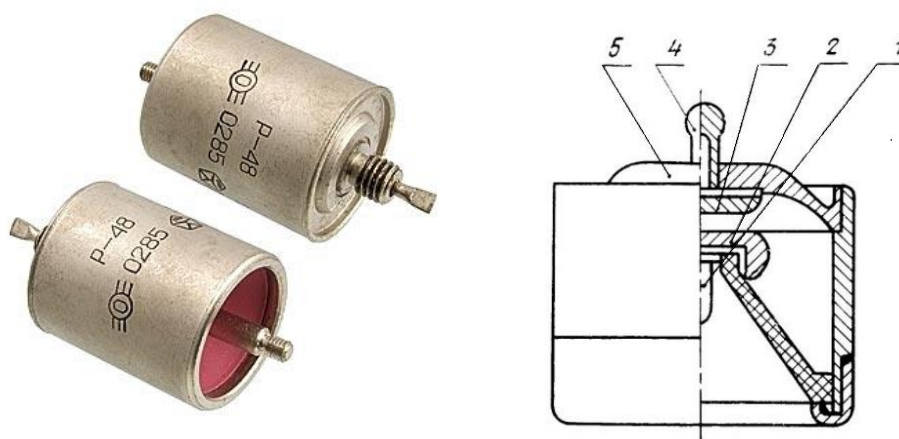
Внешний вид и сборочный эскиз разрядника серии Р-48
